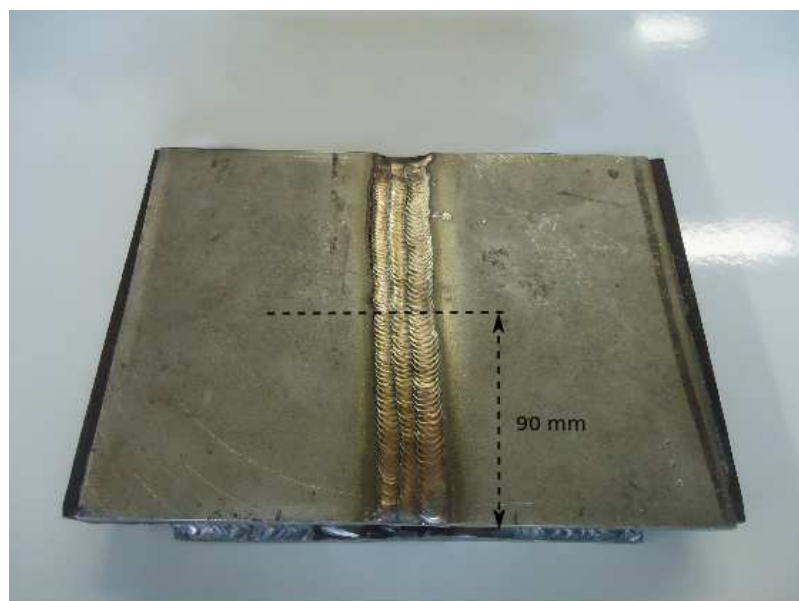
Corpo de prova 2 – Chapas de Aço Inoxidável Duplex 2205 após o processo de soldagem GTAW
